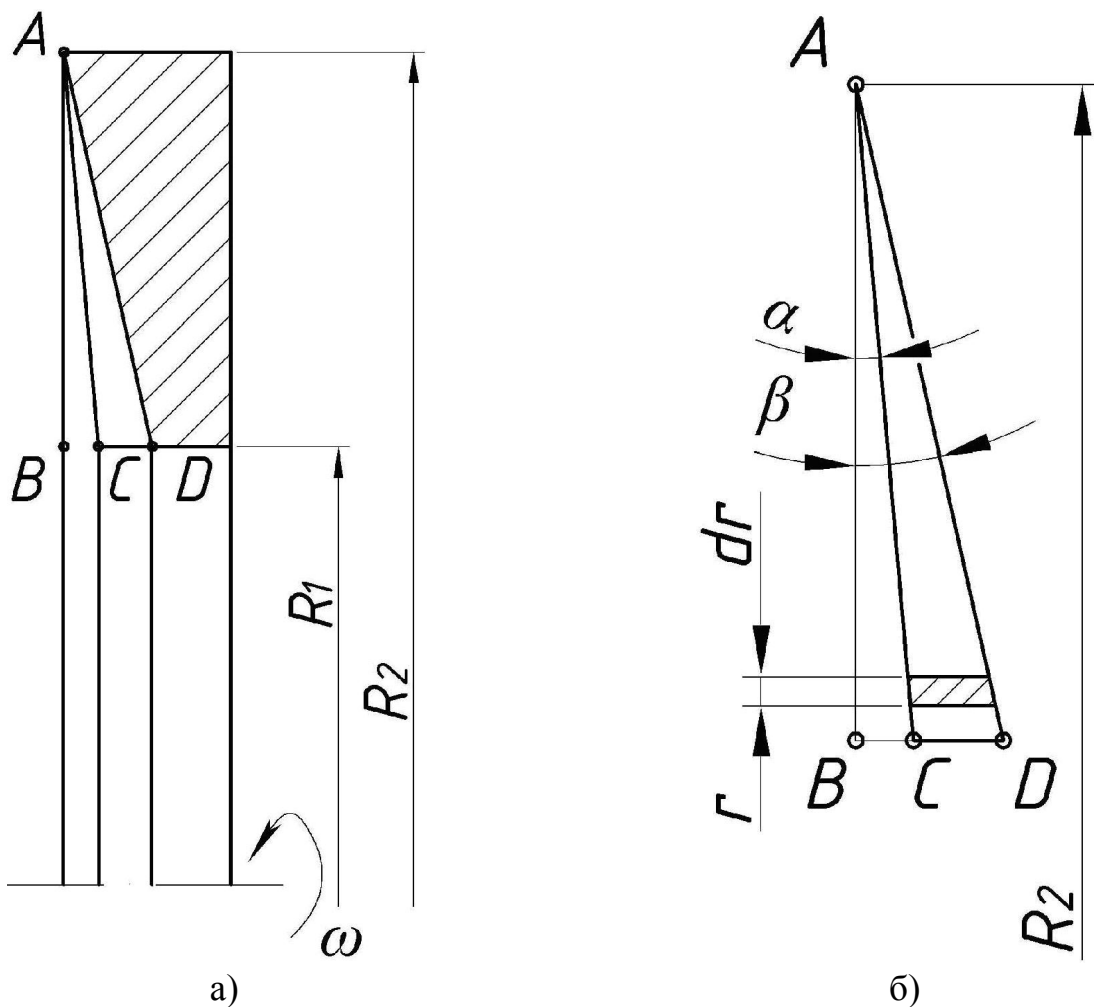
Розрахункова схема: а) загальний вигляд; б) елемент робочої поверхні
